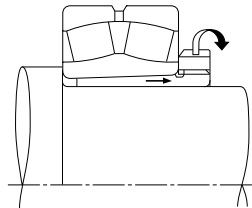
Remoção da Bucha de Desmontagem (1)
